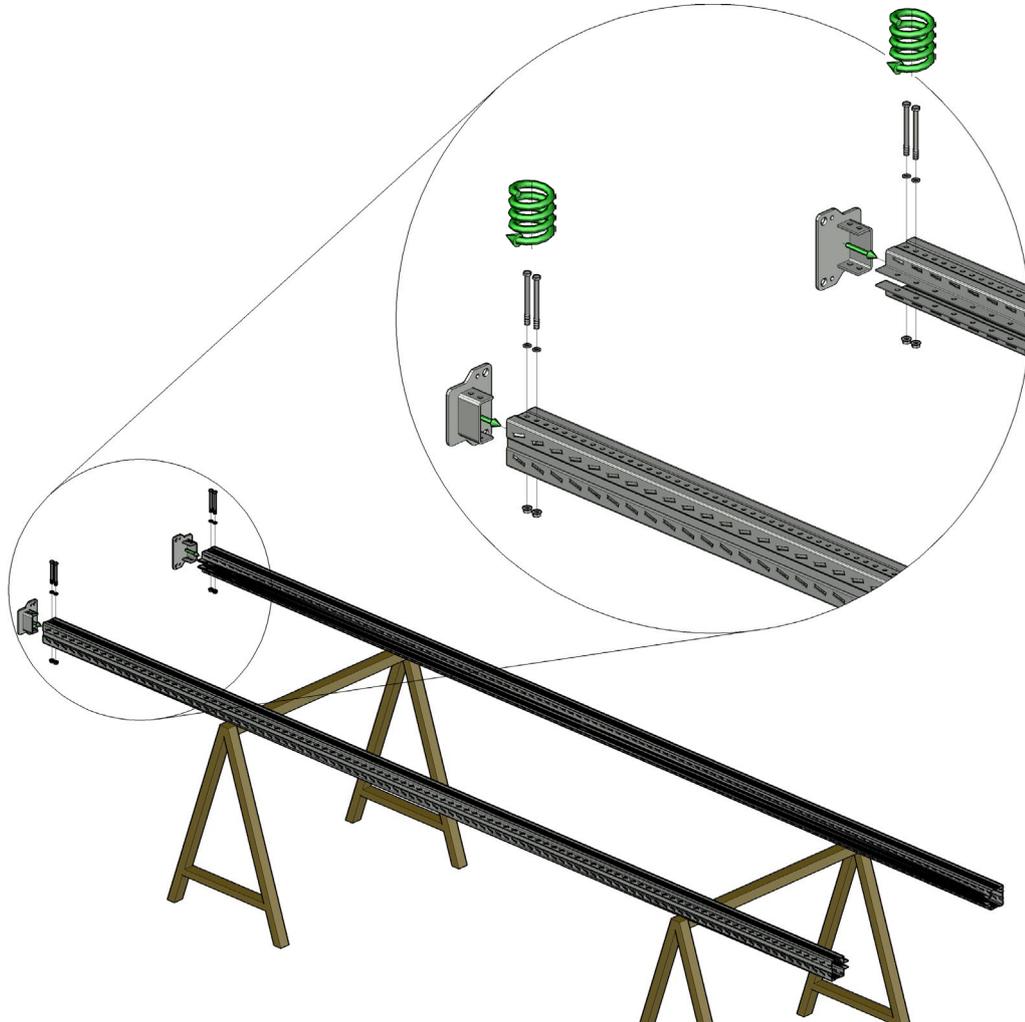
Montage der Fußplatten mit je 2 Schrauben, mit Federringen und Muttern
